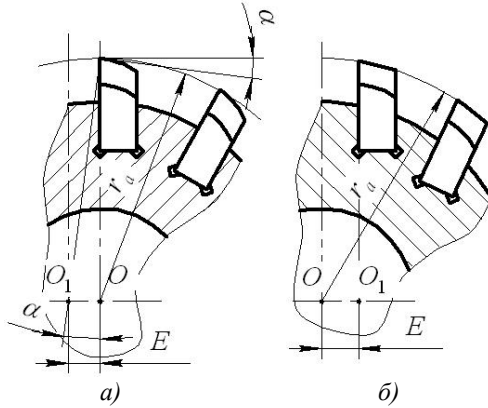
Установка зубчатых реек в рабочем (а) и технологическом (б) корпусах
